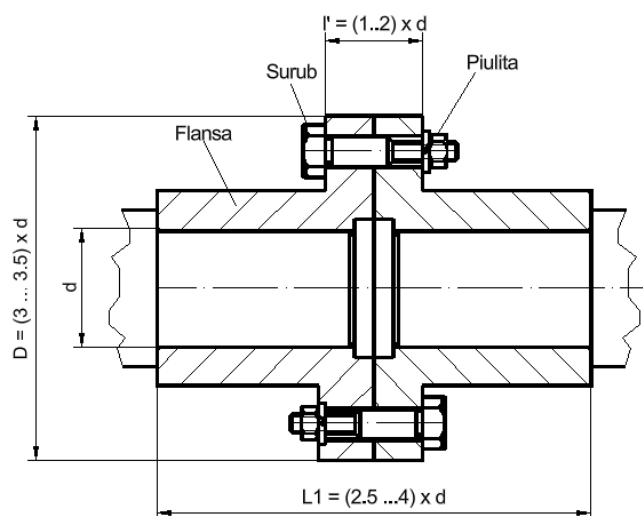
Cuplaj cu flanșă (montaj fără joc) [18]
